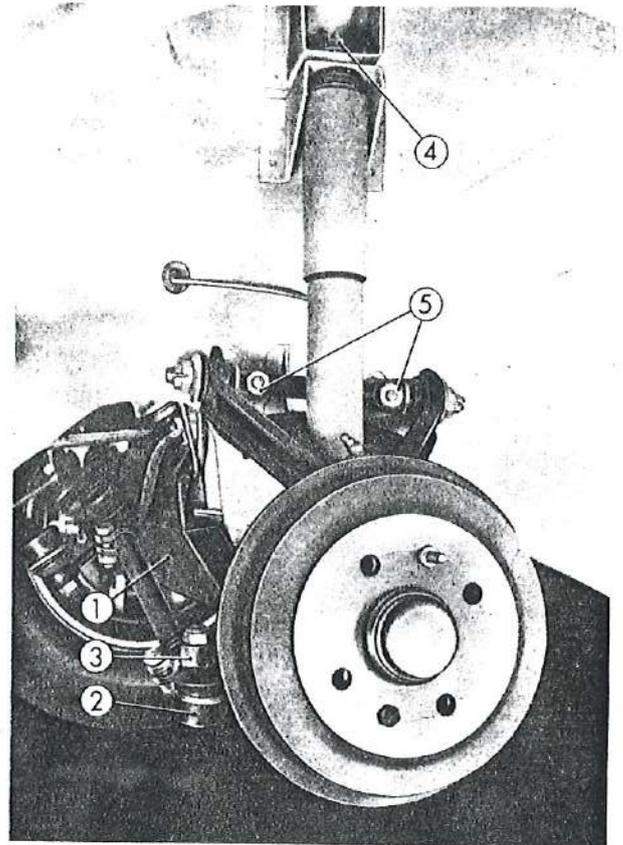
Detalle de la colocación de la suspensión, lado izquierdo del coche.
